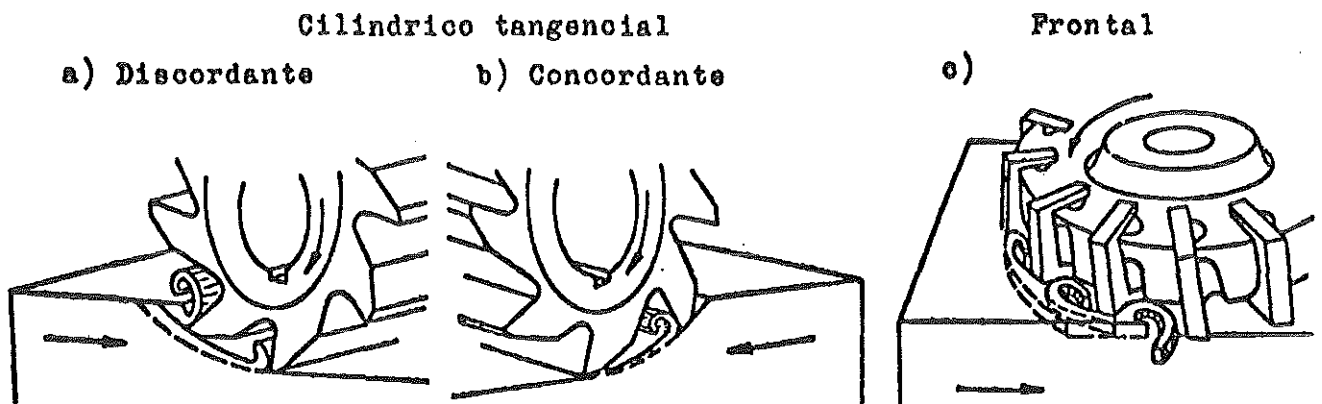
Tipos de fresamento cilíndrico tangencial e frontal.
